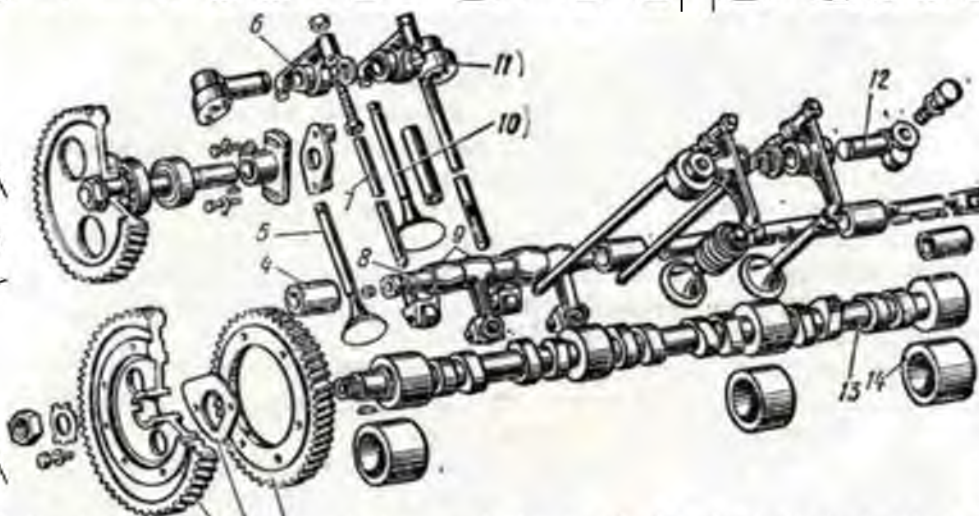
Механізм розподілу двигуна ЯМЗ-236 1 - шестерня привода паливного насоса високого тиску; 2 - упорна пластина; 3 - шестерня привода розподільного валу; 4 - втулка осі штовхачів; 5 - клапан; 6 - коромисло; 7 - штанга; 8 - вісь штовхачів; 9 - штовхачі; 10 - напрямна втулка; 11 - стійка осі коромисел; 12 - вісь коромисла; 13 - розподільний вал; 14 - втулка підшипника розподільного валу
